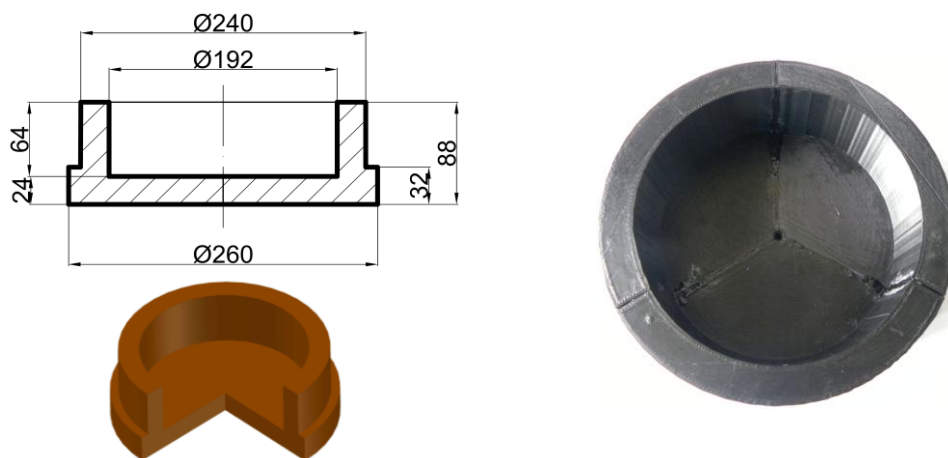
Модель струегасителя для приема струи металла из сталеразливочного ковша
